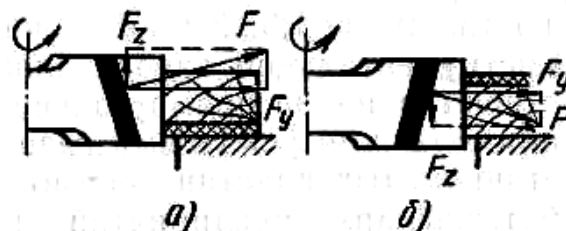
Схема расположения наклона режущих кромок фрезы к детали с облицовочным материалом, расположенным снизу (а) и сверху (б)
